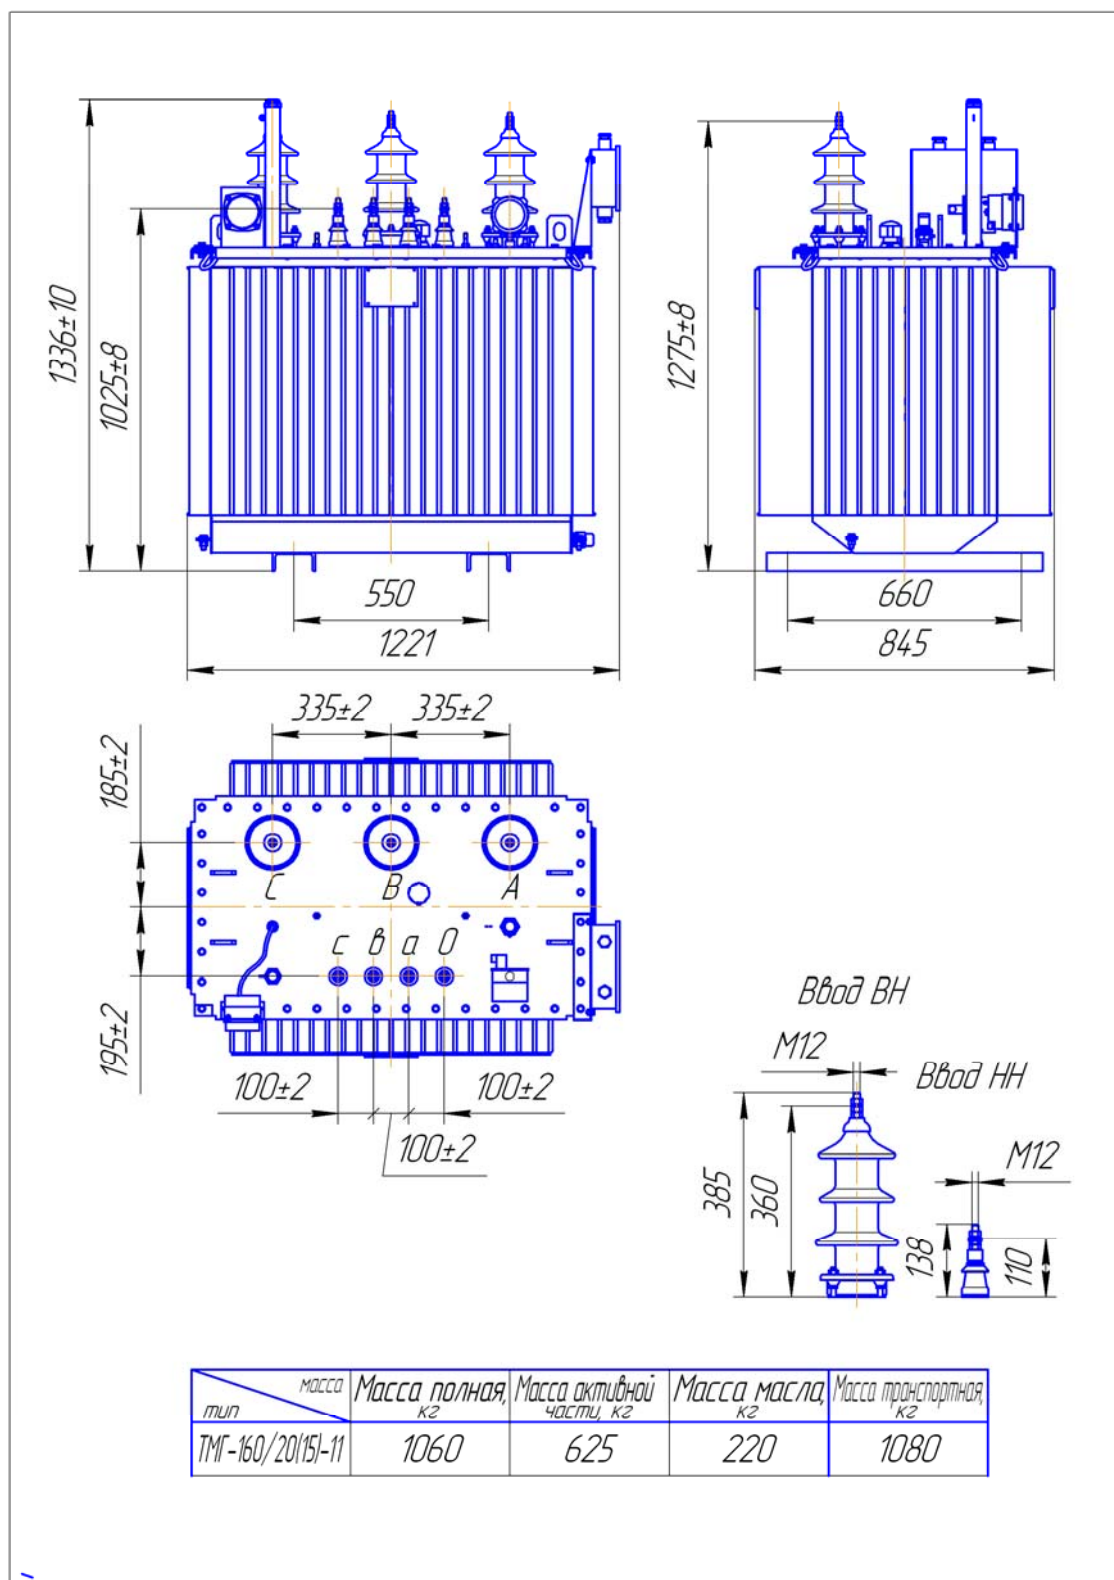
Габаритные, установочные и присоединительные размеры трансформатора ТМГ - 160/20-11
